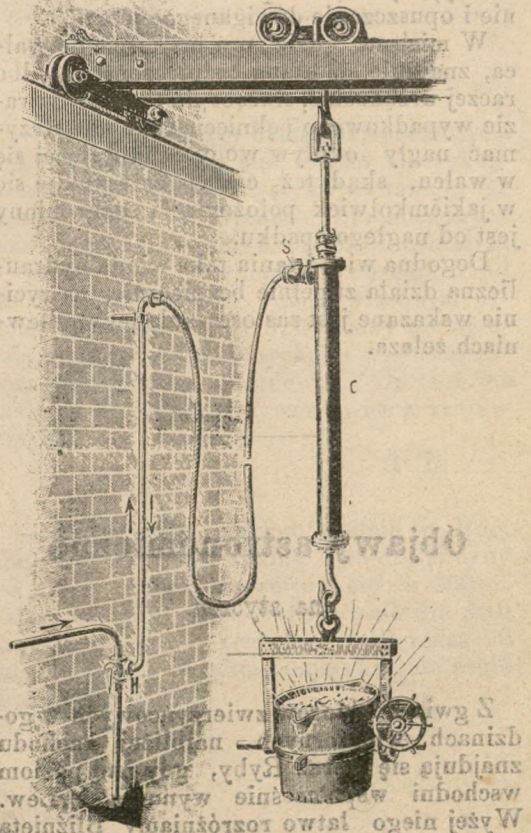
Winda hydrauliczna w walcu w żelaza.
